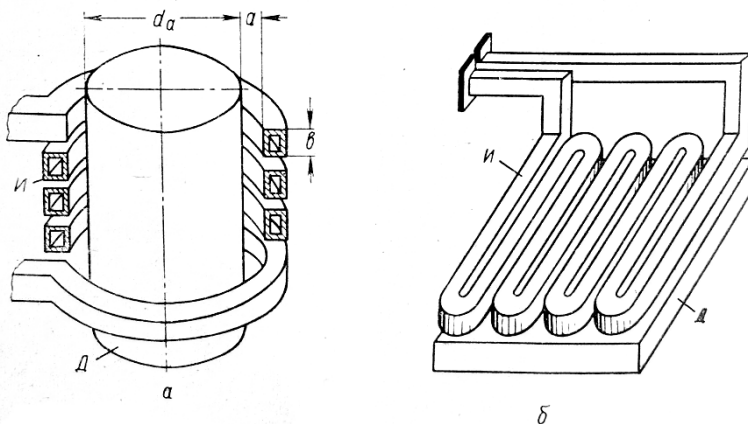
Индукторы: а – цилиндрический; б – петлевой для нагрева плоских деталей; И – индуктор; Д – деталь.
